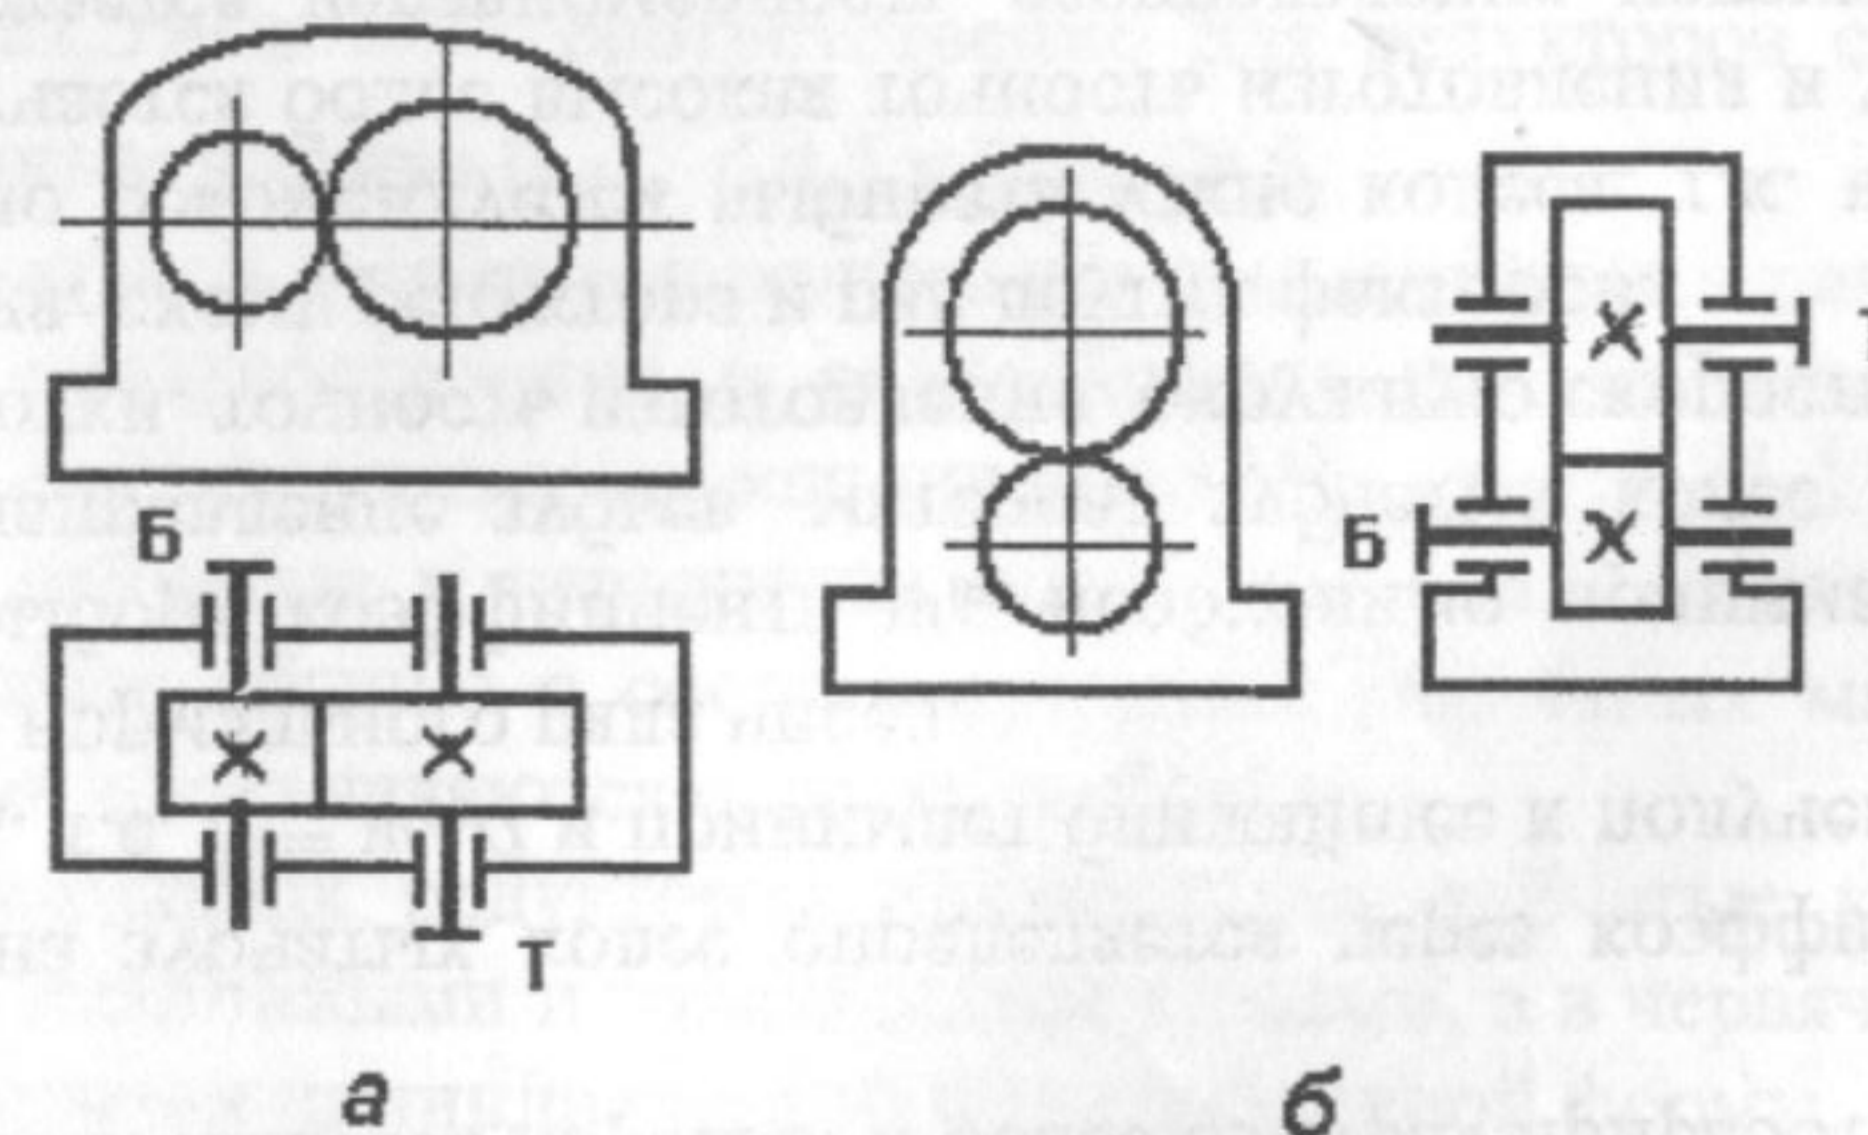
'. Кинематические схемы цилиндрических одноступенчатых редукторов
